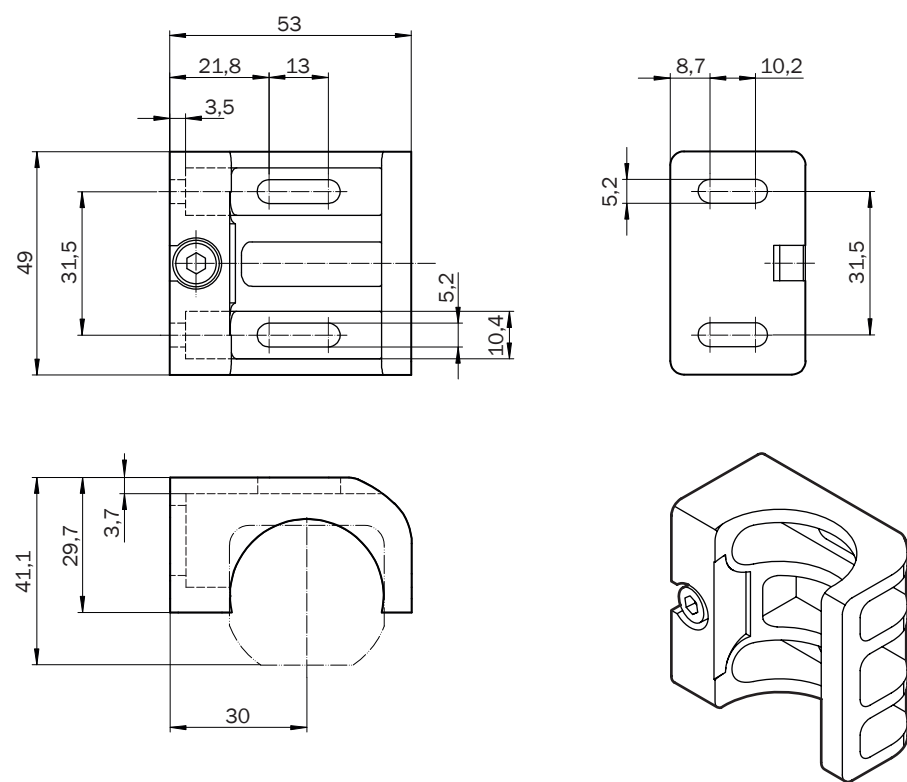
Plan coté de la fixation FlexFix (2066614)
